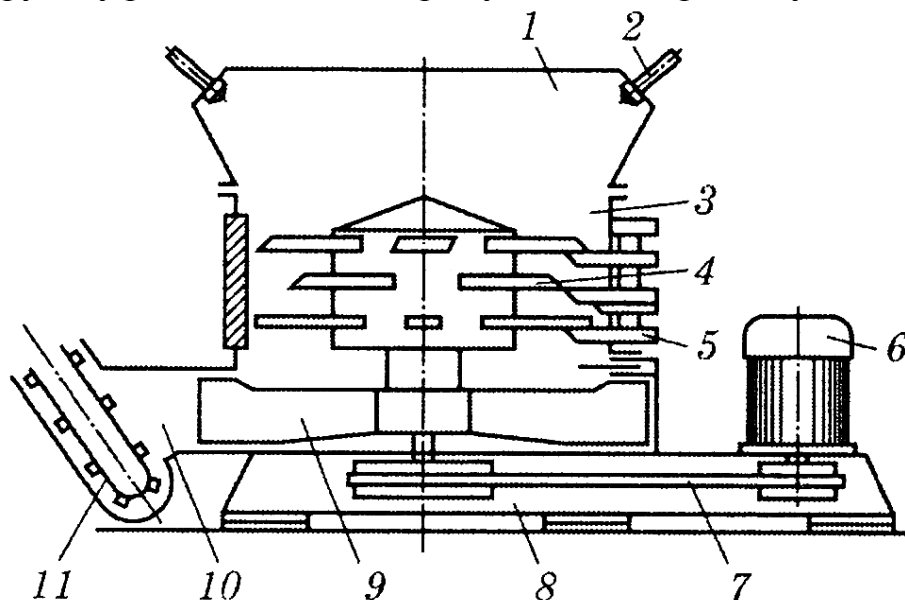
Конструктивна схема подрібнювача-змішувача кормів ИСК-3А: 1 – приймальна камера; 2 – розбризкувач; 3 – робоча камера; 4 – ротор з ножами; 5 – нерухомі ножі (протиризів); 6 – електропривод; 7 – клинопасова передача; 8 – рама; 9 – лопатева кидала; 10 – розвантажувальна камера; 11 – транспортер
